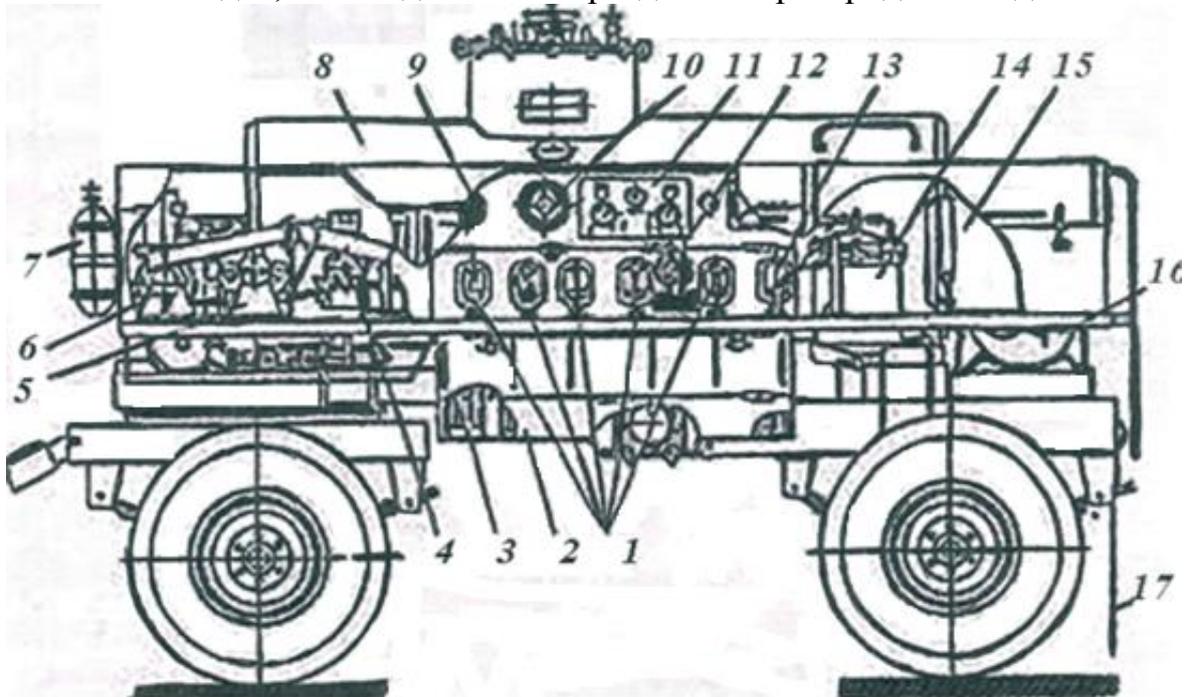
Схема заправочного агрегата типа МЗ-3904
